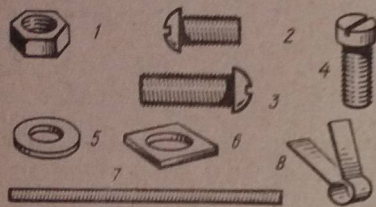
Крепежные детали: 1 — гайка шестигранная; 2 — винт короткий; 3 — винт длинный; 4 — винт установочный; 5 — шайба; 6 — гайка квадратная; 7 — шпилька; 8 — пружинная обойма
